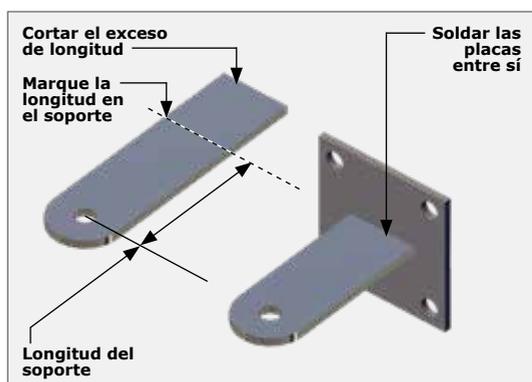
CORTAR Y SOLDAR EL SOPORTE DE PARED
